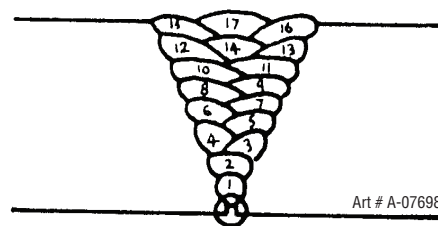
Séquence d'élaboration de la soudure
